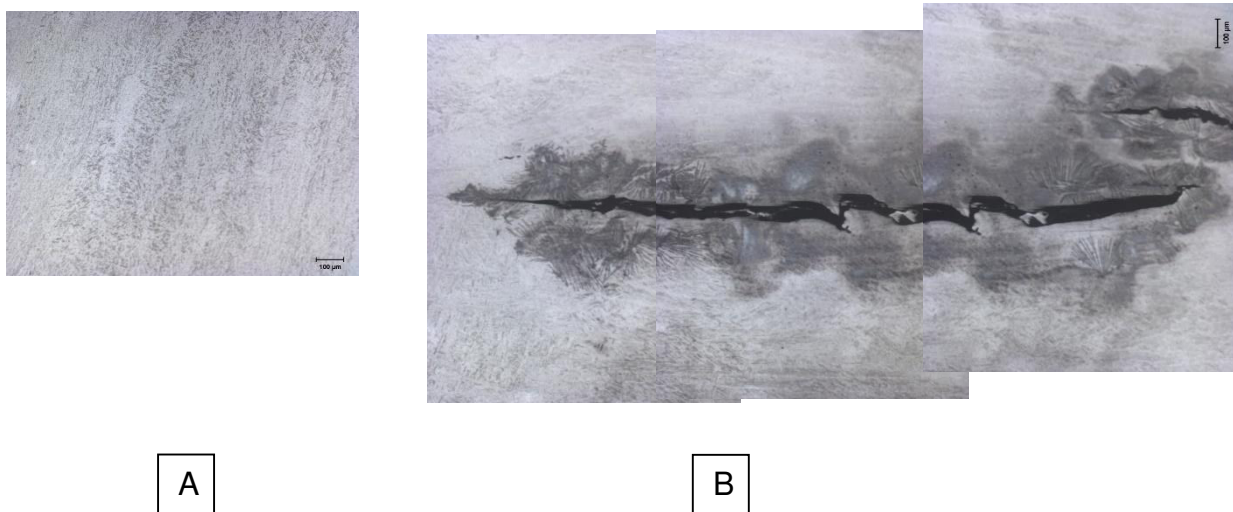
M6, soldadura contacto, KALLING'S, 100X. Imágenes. A.-Tamaño de grano 6 ASTM presente una solidificación en forma de columna en forma de dendritas B.-Grietas presentes en la soldadura.
